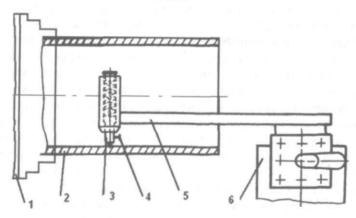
Схема фрикционного латунирования втулки: 1 — токарный патрон; 2 — втулка; 3 — латунный пруток; 4 — приспособление; 5 — борштанга; 6 — держатель токарного станка
